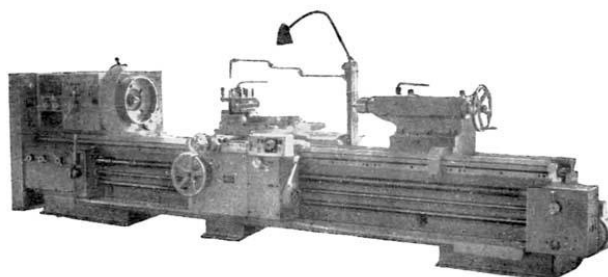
Токарно-винторезный станок 16К30 класс точности станка по ГОСТ 8-77.
